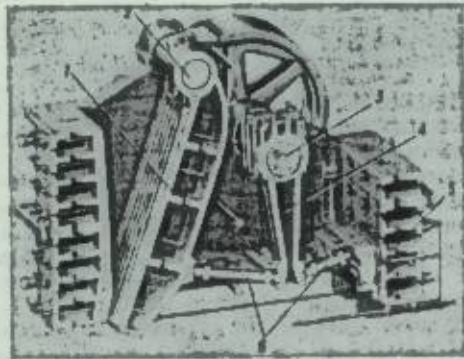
Типовая конструкция дробилки с простым движением подвижной щеки.
